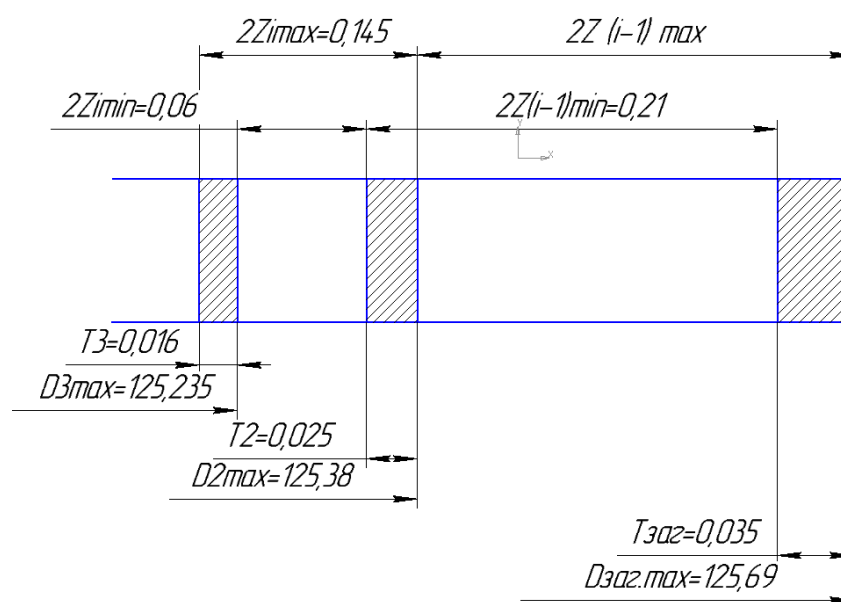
Схема расположения припусков, допусков и размеров
